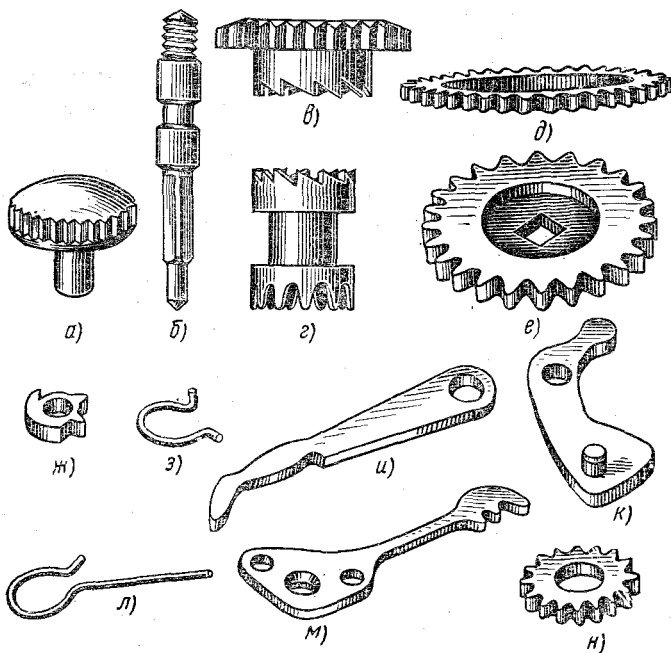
Детали механизма заводки часов и перевода стрелок:
